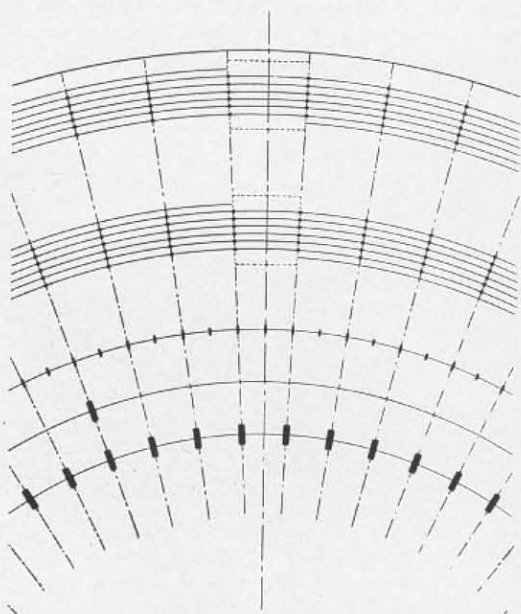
Scheibe des Abtasters für die Zwillingmaschine.
